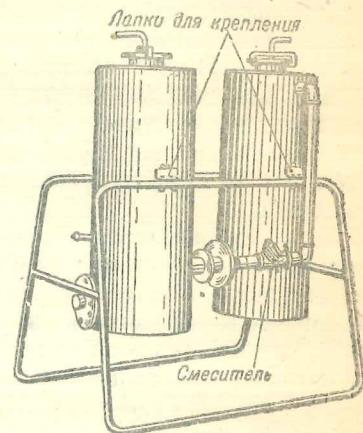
Общий вид газогенераторной установки ГКП-2Ш
